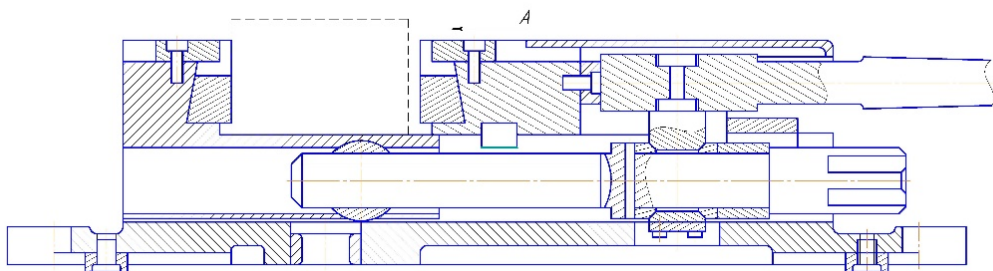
Схема компоновки (общий вид) приспособления
